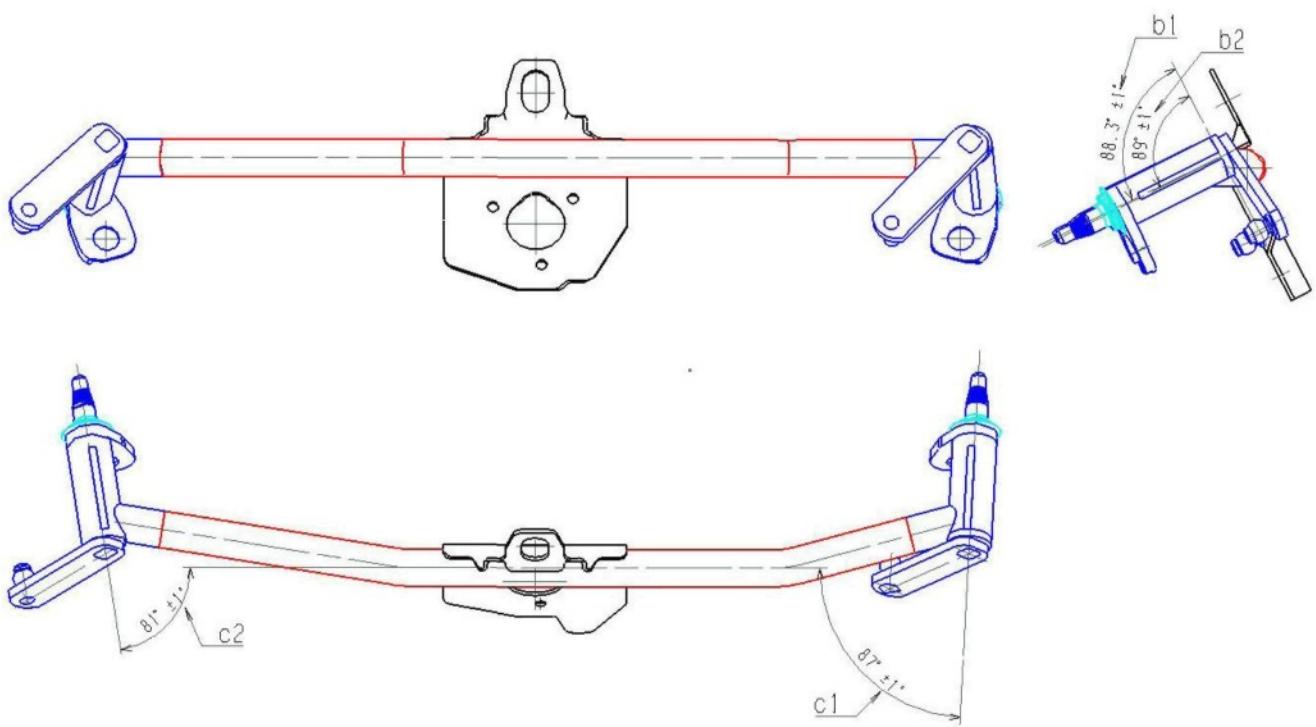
Natočení stěračové soupravy vlivem tolerance plechů – geometrický součet tolerancí
